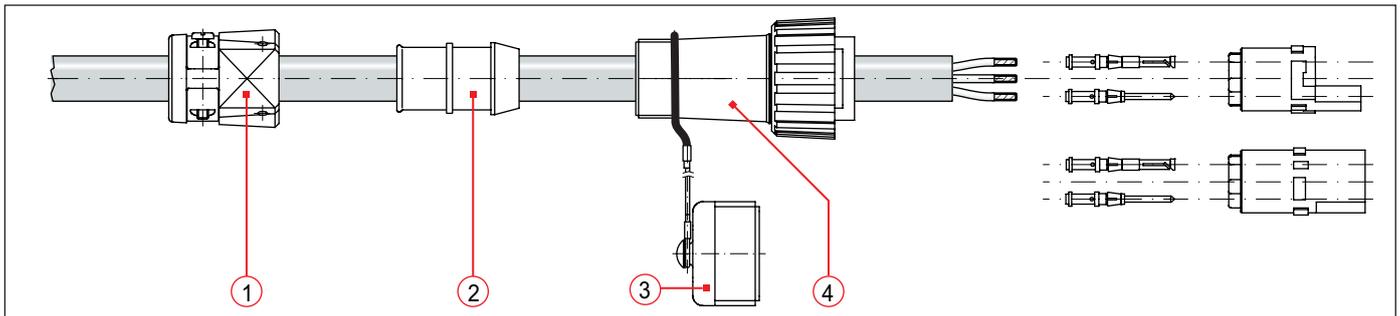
Beispiel für Stecker mit Endgehäuse, Zugentlastung und Verschraubung (gilt analog auch für Kabel Dosen)
